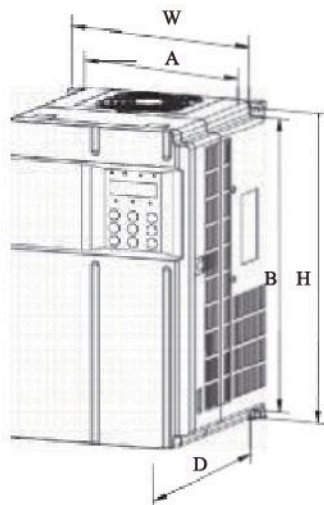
Схема габаритных и установочных размеров пластиковой конструкции
